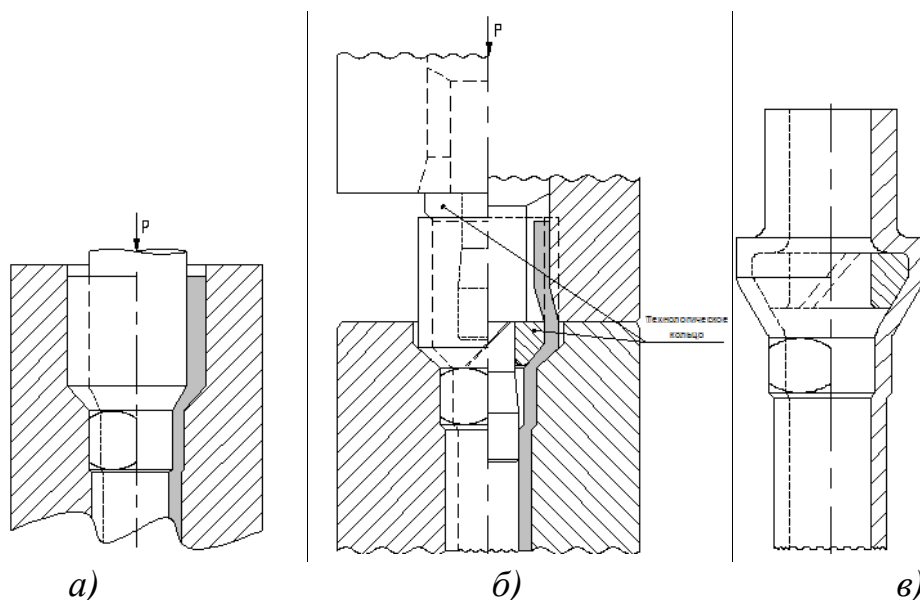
Схема формообразования полуфабриката на четвертом переходе штамповки (а), схема установки технологического кольца А в полуфабрикат (б) и головка насосной штанги после последнего перехода штамповки (в)
